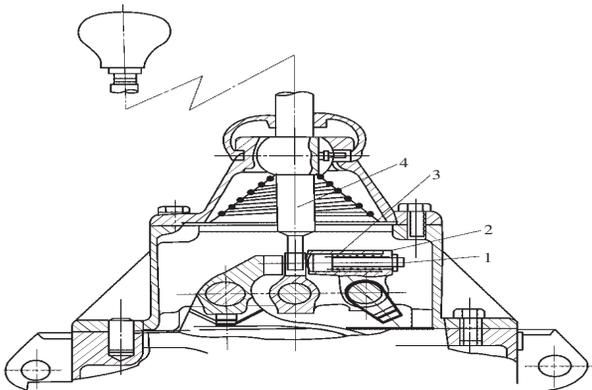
东风 EQ1090E 型汽车五挡变速器倒挡锁装置
